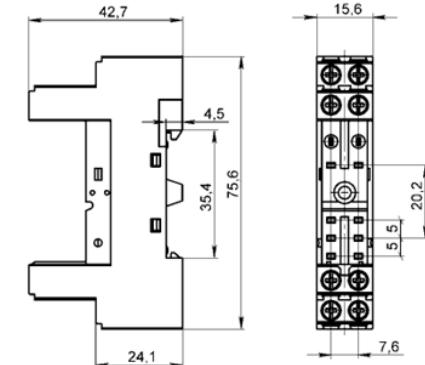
Габаритные, установочные и присоединительные размеры розетки OptiRel G RR95-82
